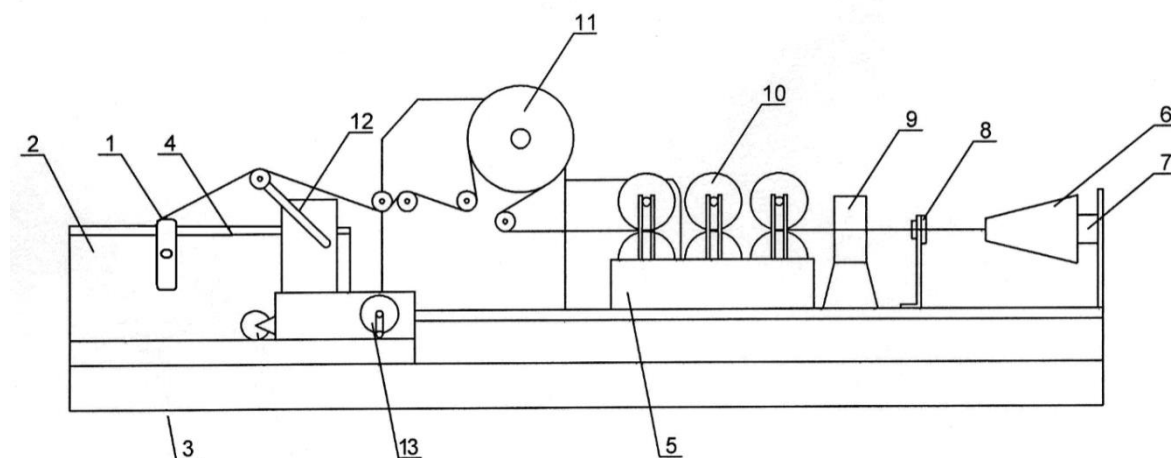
Схема установки для изготовления микропластика, где 1 – рамка для намотки микропластика; 2 – редуктор; 3 – стойка; 4 – двигатель; 5 – пропиточная ванна; 6 – паковка с армирующим материалом; 7 – шпулдержатель; 8 – фильера; 9 – нитенаправитель; 10 – ролики пропиточной ванны и отжимные ролики; 11 – узел натяжения; 12 – раскладчик; 13 – счетчик
